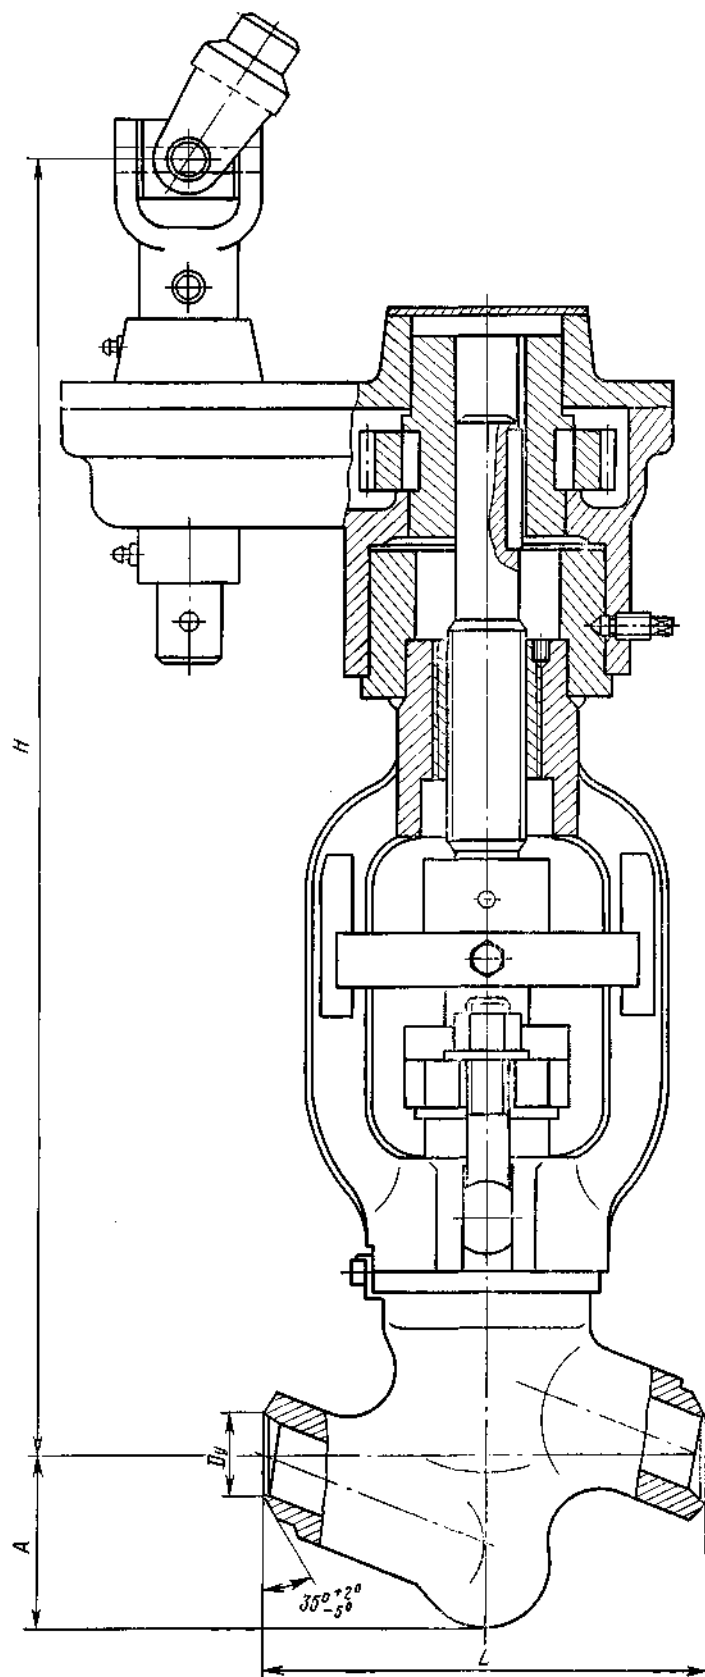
Вентиль с приводной головкой и цилиндрической зубчатой передачей D, 40, 50 и 65
